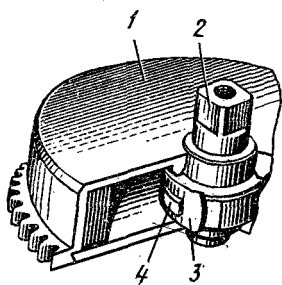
Крепление внутреннего конца пружины на валу барабана:
